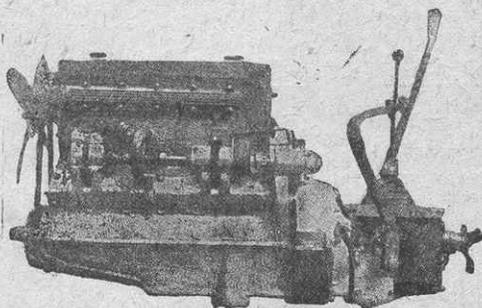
Шестицилиндровый двигатель с коробкой передач «Крупп» 90 л. с.
